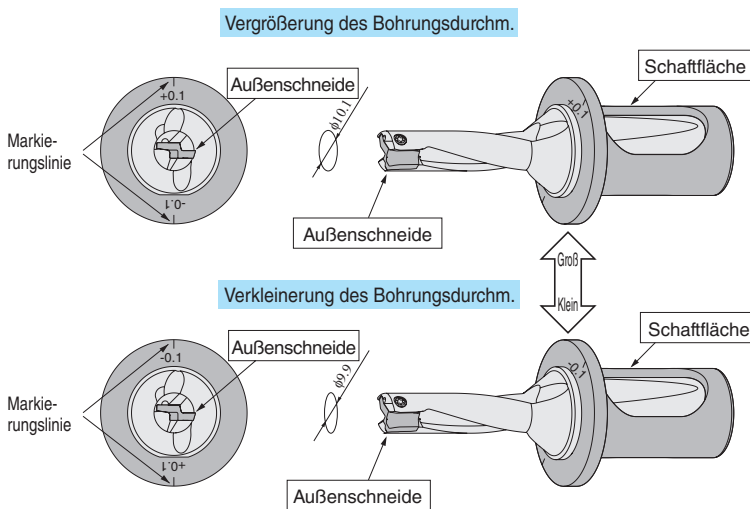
Methode zum Einstellen des Bohrungsdurchmessers (Beispiel)  $\varnothing 10$ -Bohrer
